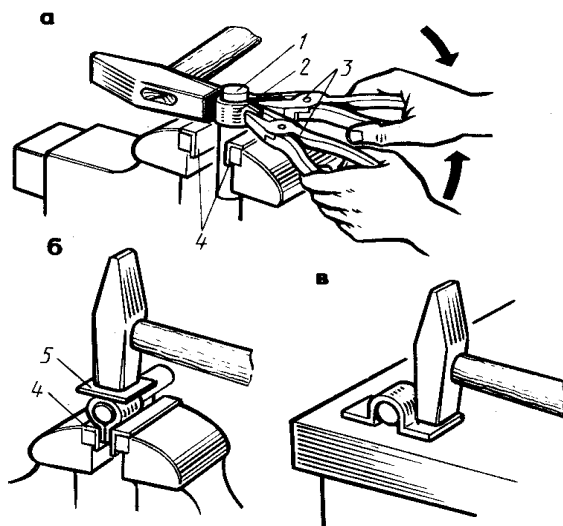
Приемы гибки хомутика: 1 – оправка; 2 – заготовка; 3 – плоскогубцы; 4 – нагубники; 5 – медная пластина
